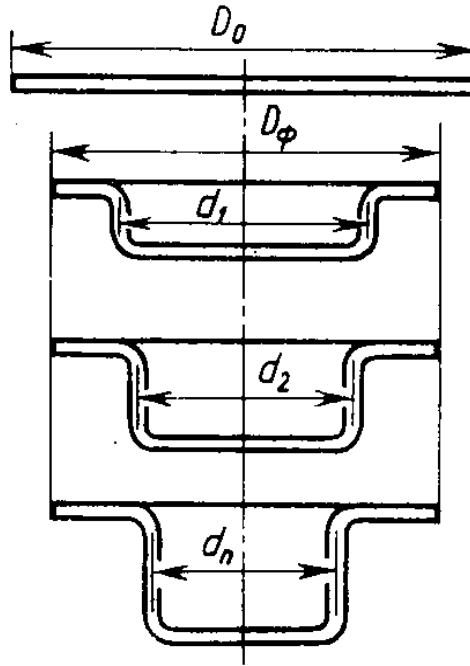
Переходи витягування заготовок з широким фланцем: D_0 – діаметр вихідної заготовки; D_ϕ – діаметр фланця заготовки; $d_1, d_2 \dots d_n$ – діаметр циліндра на n -ному переході
